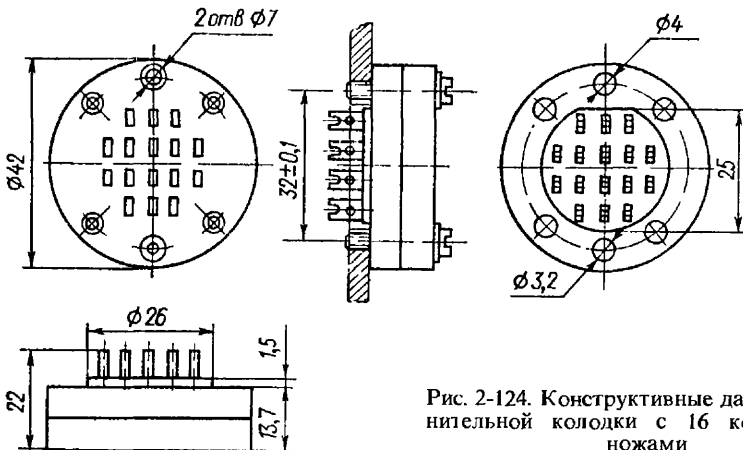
Конструктивные данные соединительной колодки с 16 контактными ножами
